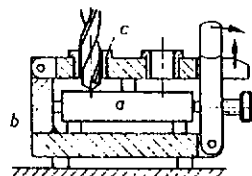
Montaje para taladrar. a) Pieza; b) montaje para taladrar; c) casquillos para guía de la broca.
